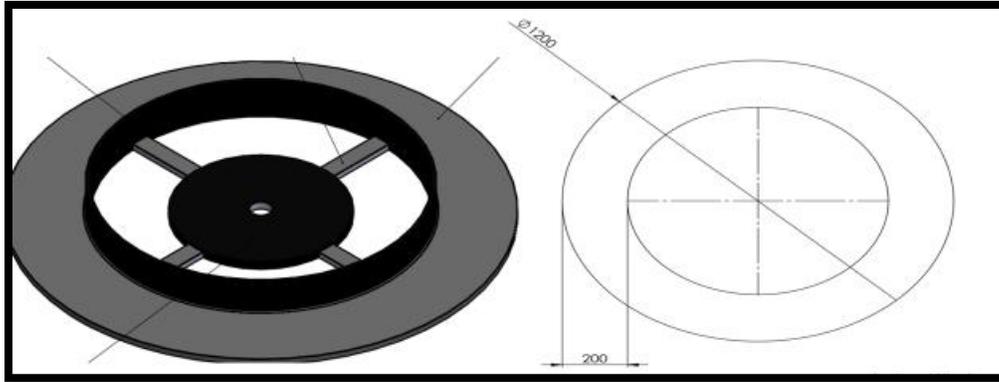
Dimensiones de la base de la cámara de selección.
